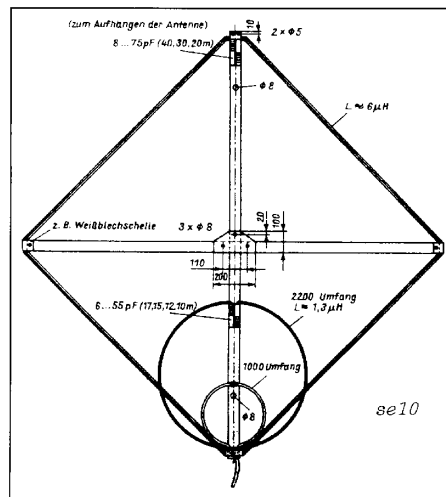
Twee ramen, het ene voor 20, 30 en 40 m en het andere voor 10 t/m 17 m, met gemeenschappelijke koppellus. Tijdens transport kan de bovenste helft van het ruitvormige raam naar beneden worden geklapt. Een constructie van Y51UO uit *Funkamateer* 8/91.
